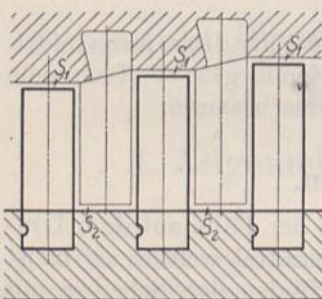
Ausschnitt aus einer Trommelturbine.
